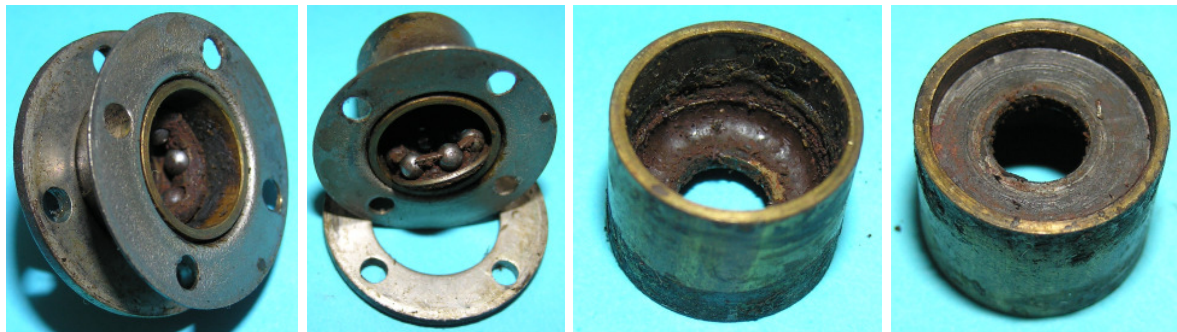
Konstruktionselemente am Lagerhalsfuß
